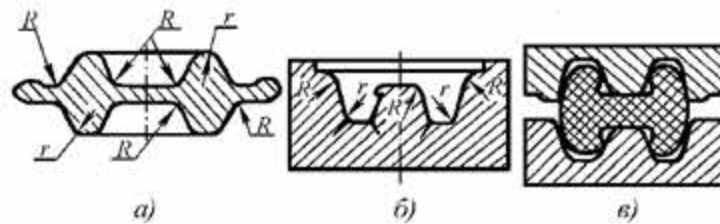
Розташування радіусів закруглень на поковках
